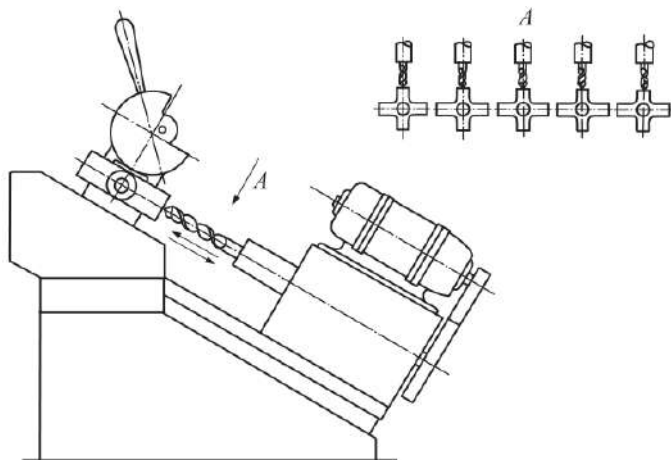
Схема налагодження верстата ВА26 для свердління отворів у п'яти деталях
